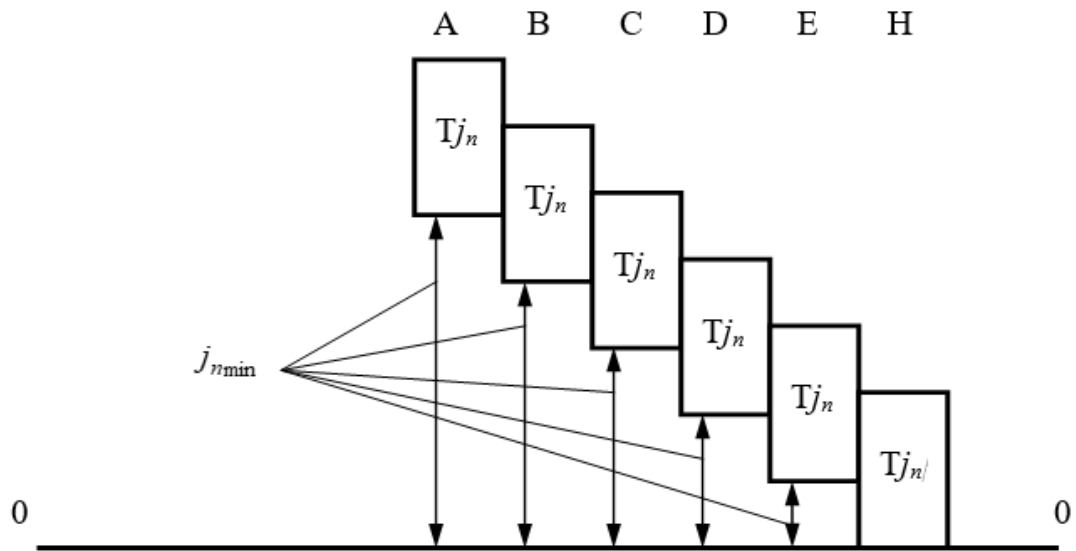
Схема розташування поля допусків Tj_n для прийнятих різновидів спряження по боковому зазору
